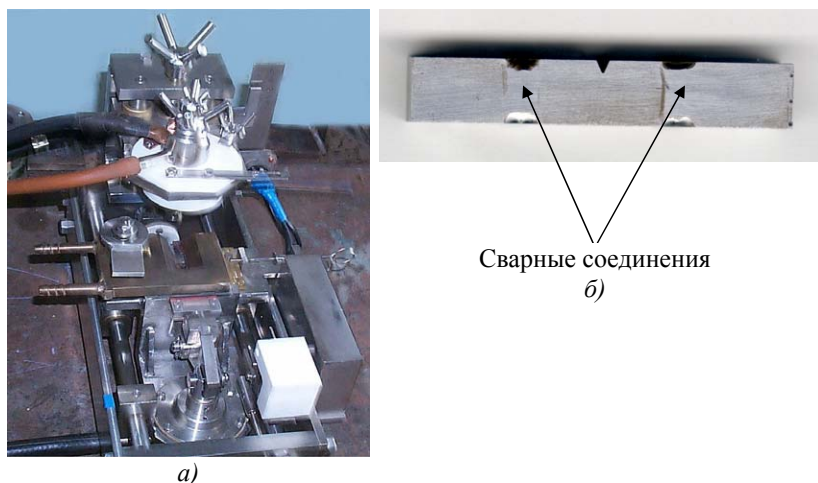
Установка сварки САУ-АДС для реконструкции ударных образцов Шарпи (а) и ударный образец (б), прошедший реконструкцию способом аргодуговой сварки
